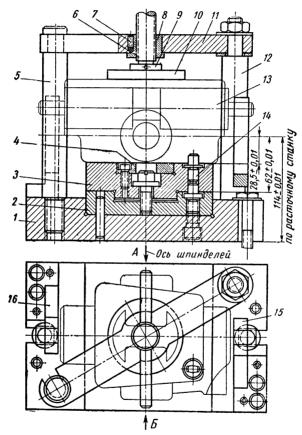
Приспособление для установки детали на алмаэнорасточном станке
